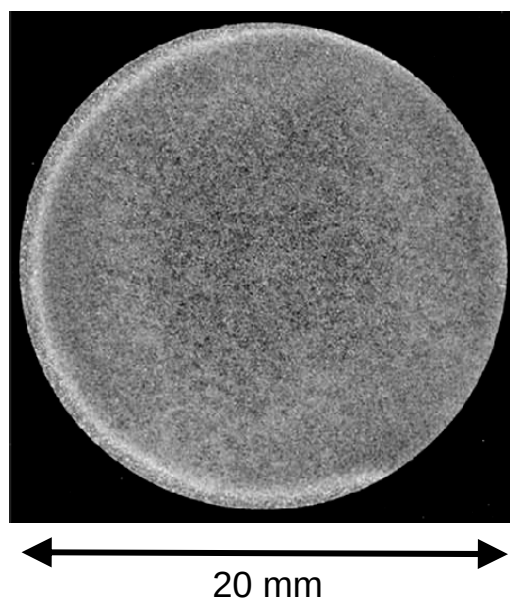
Componente cilíndrico cementado assimetricamente, 940°C, 135 min.⁽⁴⁾
